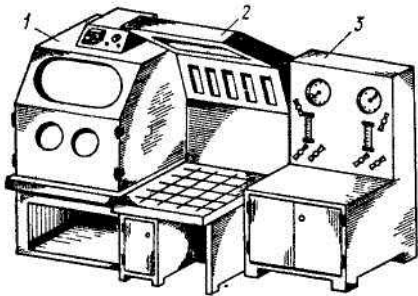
Пост газополуменового напилення порошків: 1 – установка піскоструминної обробки; 2 – зварювальний стіл; 3 – газорозподільний щит.
